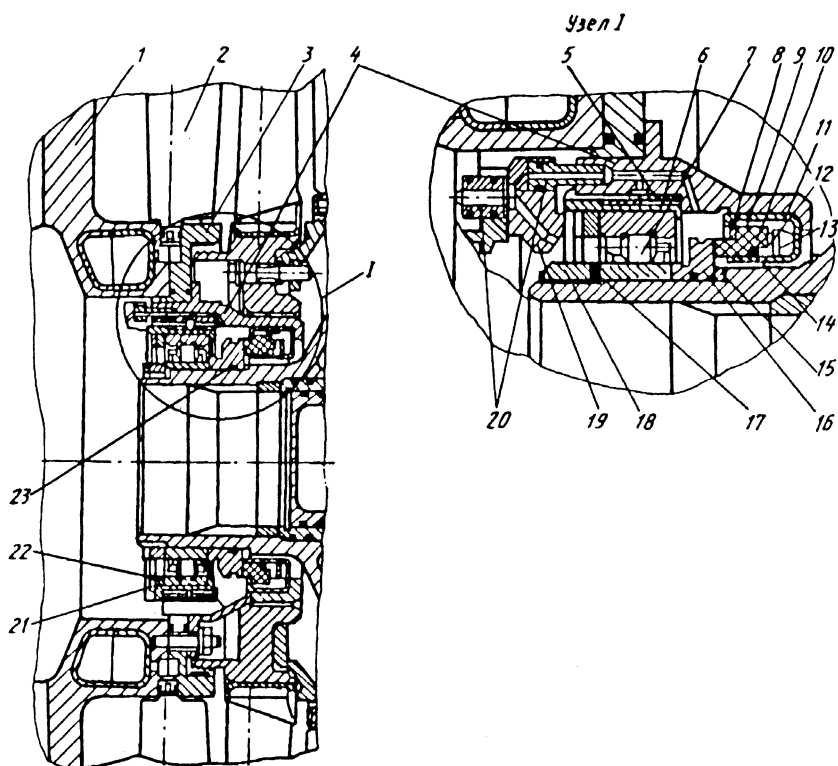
Передняя (первая) опора ротора компрессора:
